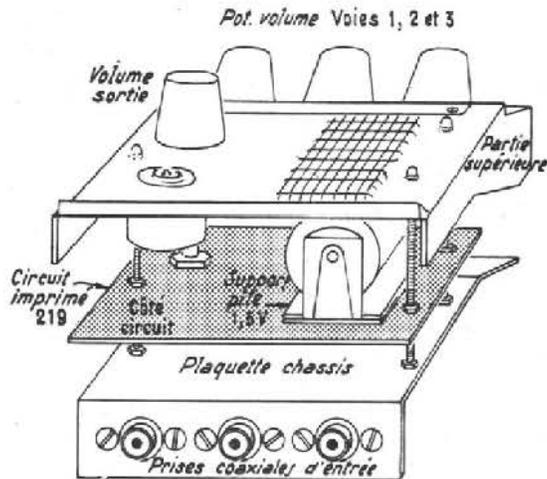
Assemblage des différents éléments du mélangeur 225
